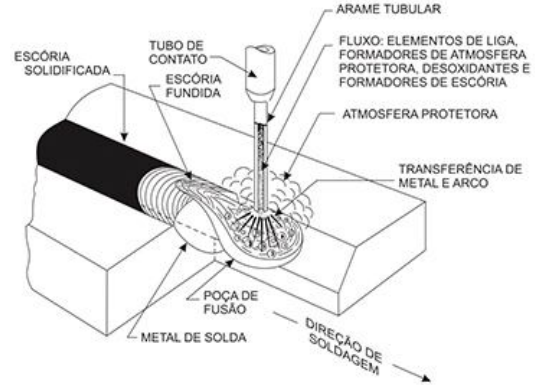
Soldagem com arames tubulares com proteção externa e Soldagem com arames tubulares autoprotetidos - Fonte: Apostila ESAB
